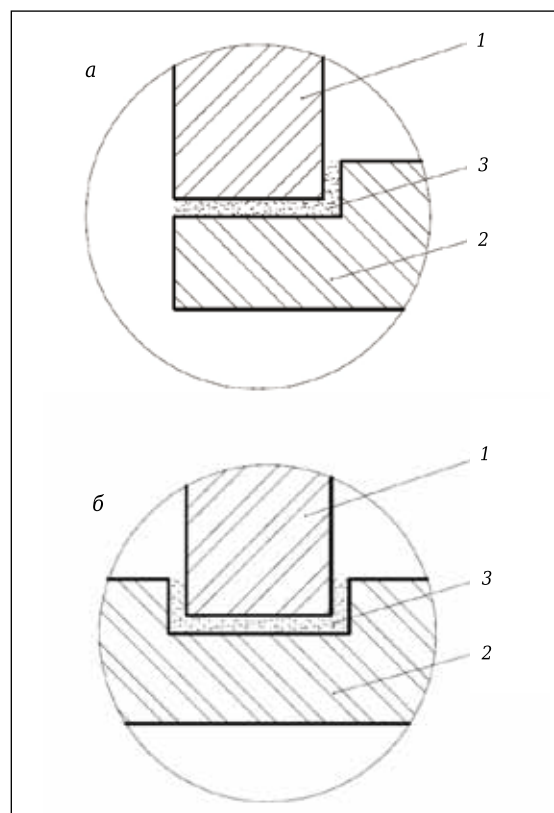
Замковое соединение между корпусом и днищем с засыпкой в виде жаропрочного мелкодисперсного порошка: а — замковое соединение Г-образной формы; б — соединение П-образной формы; 1 — корпус короба; 2 — днище; 3 — жаропрочный порошок
